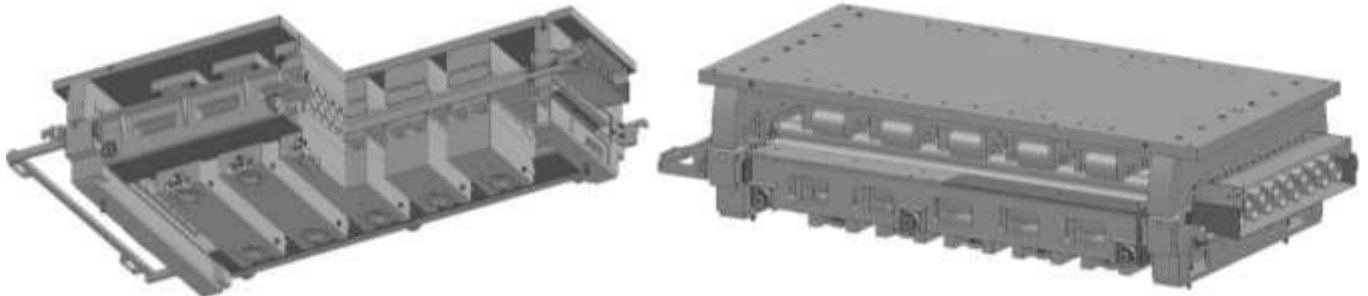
Новий комплект касет багатороликової ЛПМ агрегату поперечного різання конструкції НКМЗ
